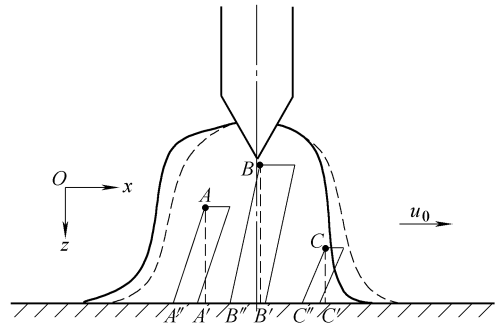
TIG 焊接运动电弧示意图(实线)
